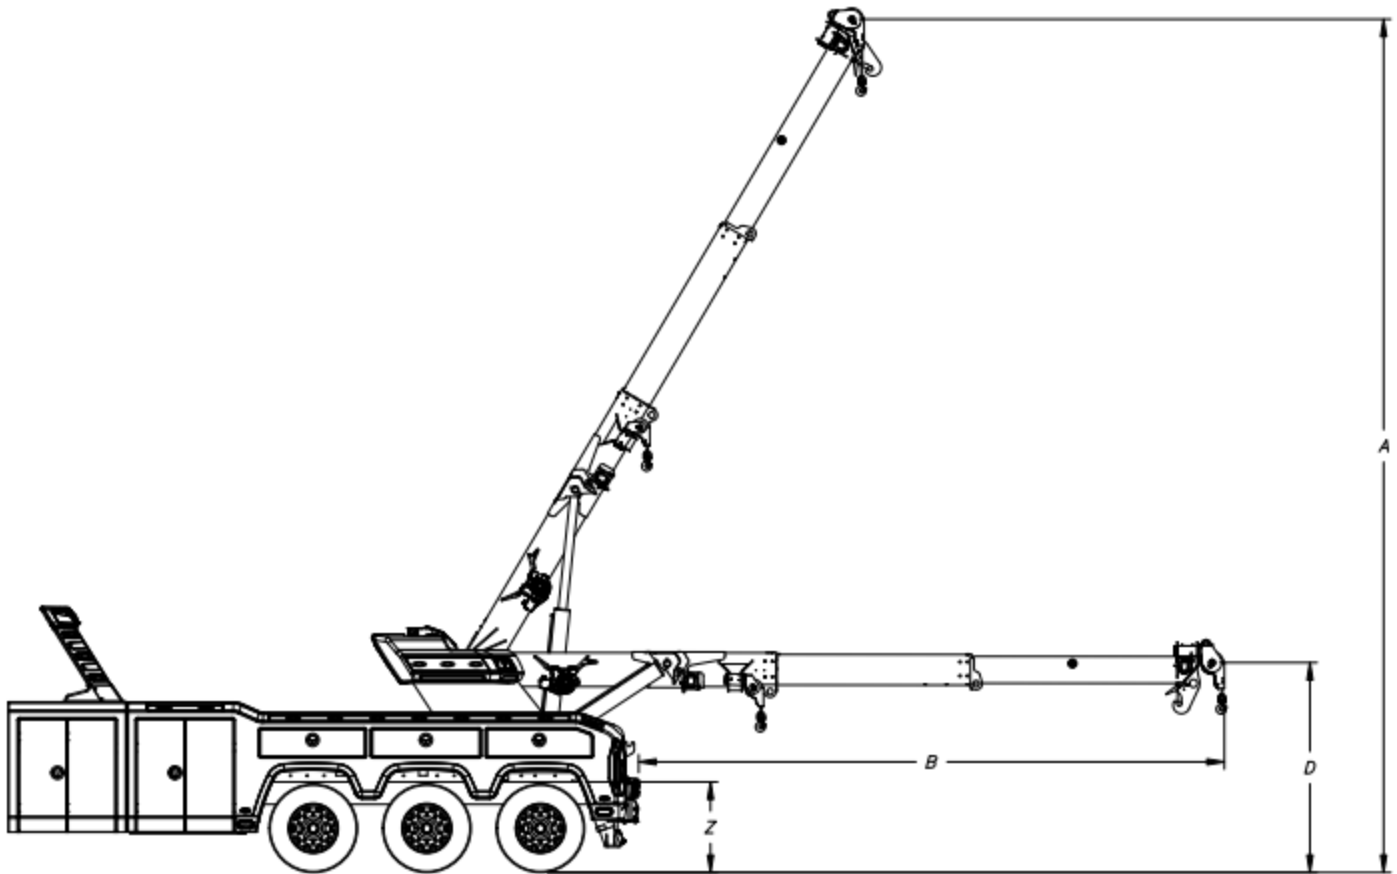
DIMENSIONS DE LA FLÈCHE ET DES BÉQUILLES - VUE LATÉRALE (EXEMPLE)
